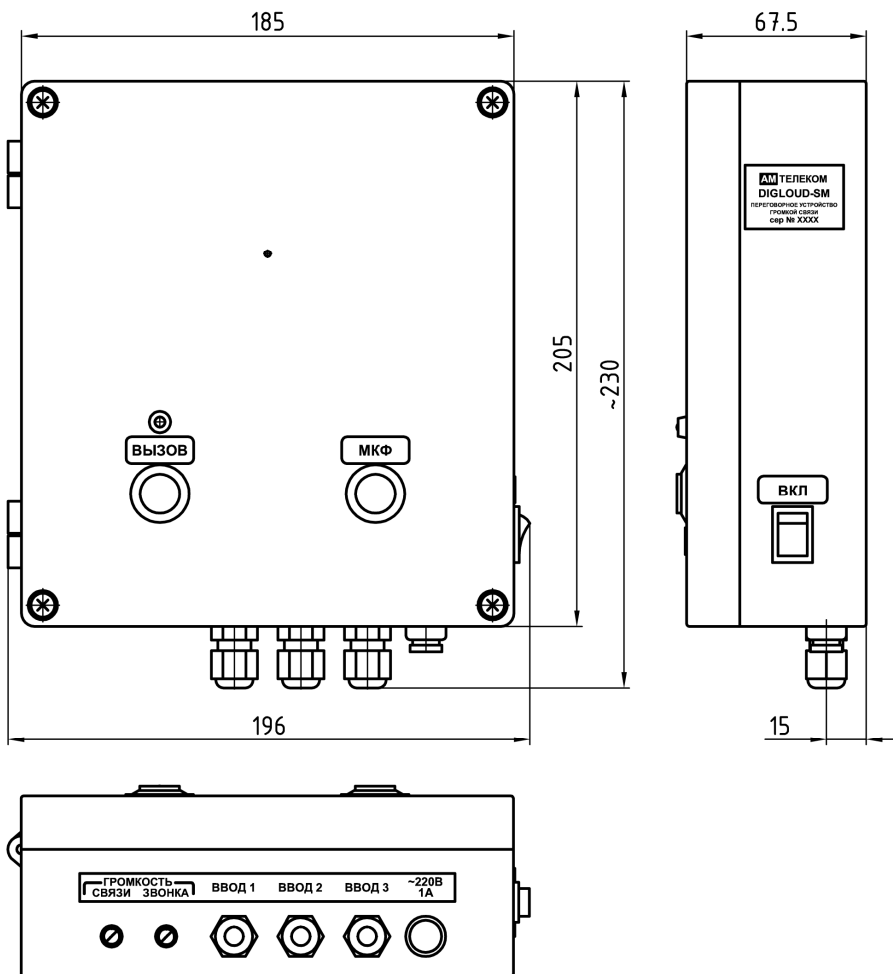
Внешний вид и габаритные размеры устройства DIGLOUD-SM.
